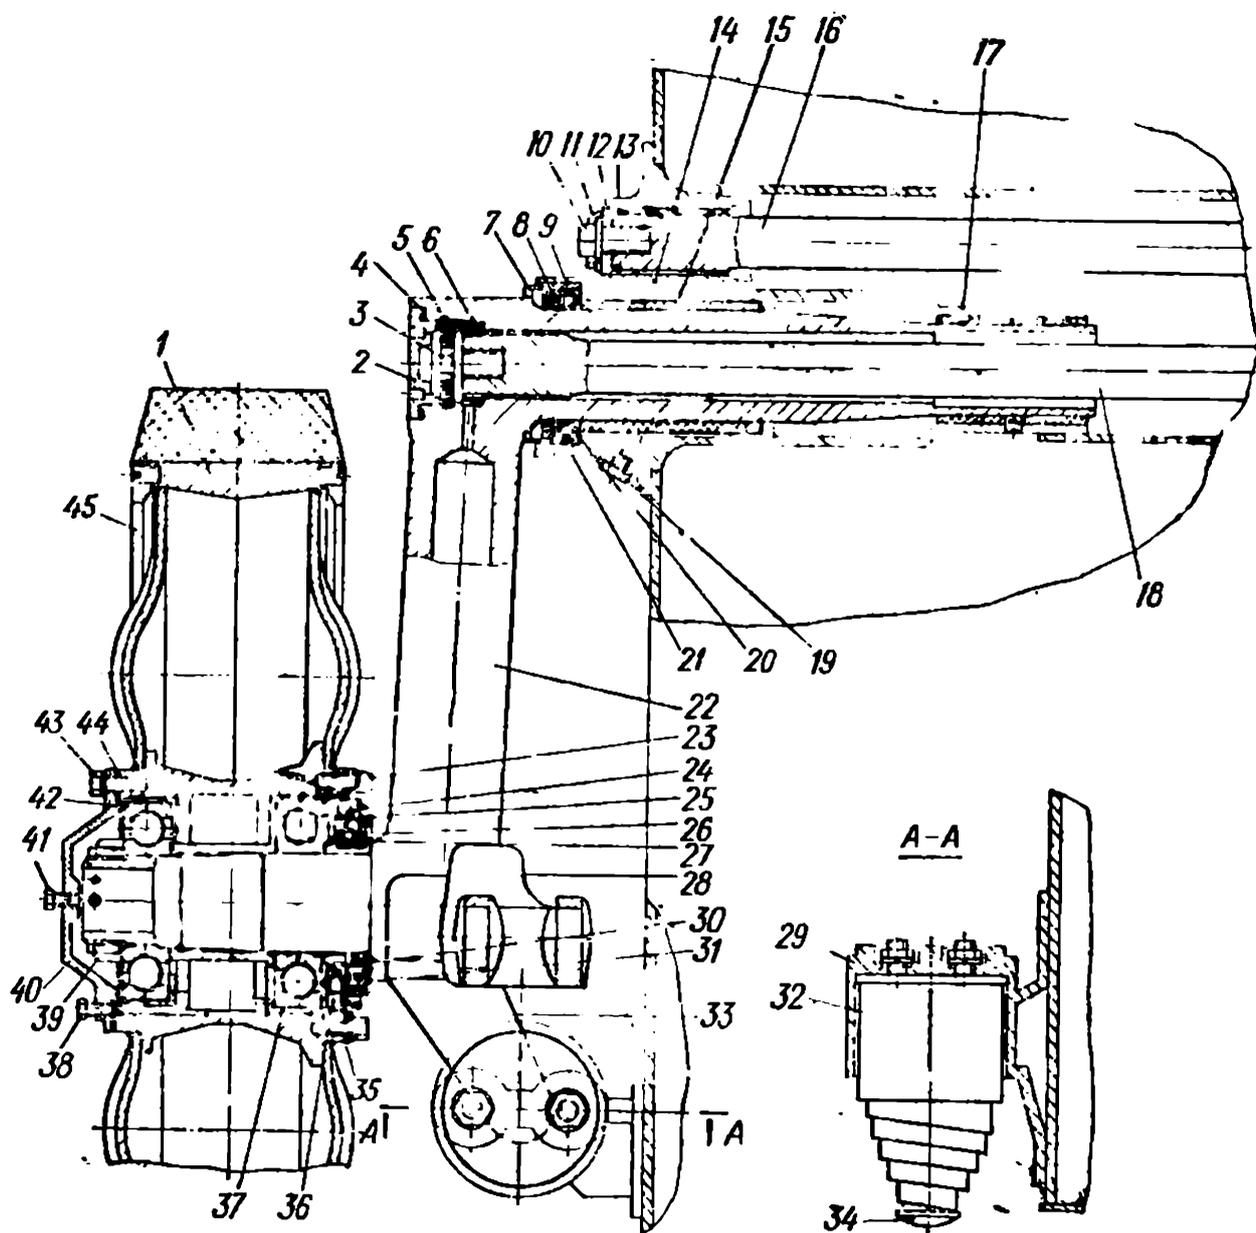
Установка опорного катка, балансира, торсиона и упора:
